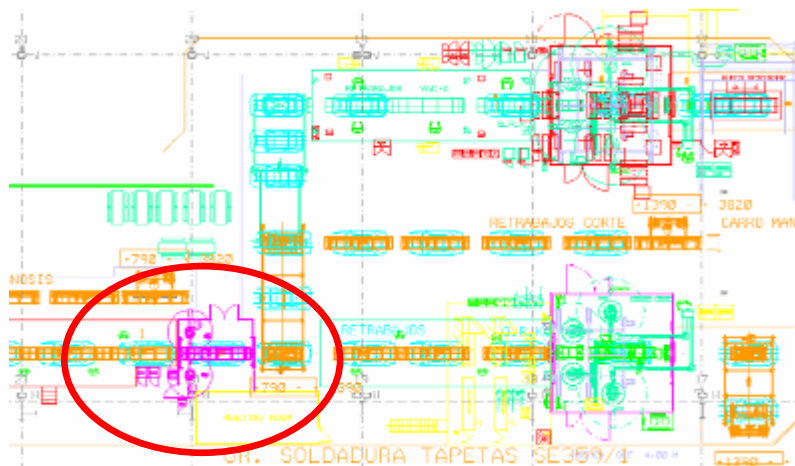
Propuesta A. Una sola instalación de soldadura
